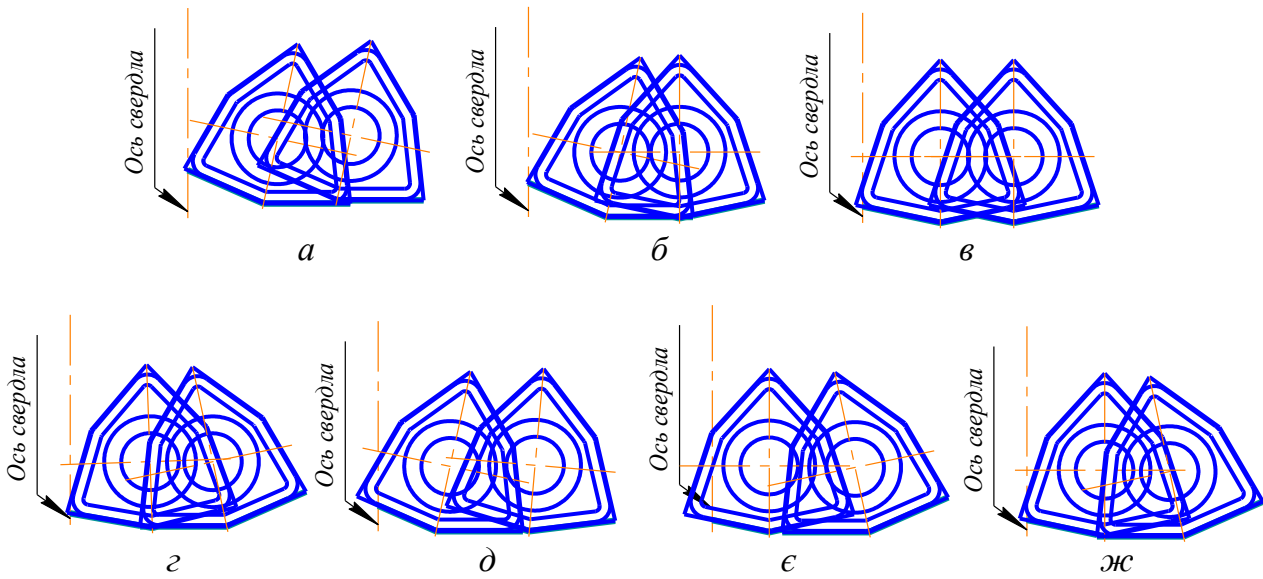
Можливі варіанти взаємного розташування різальних пластин у корпусі свердла
